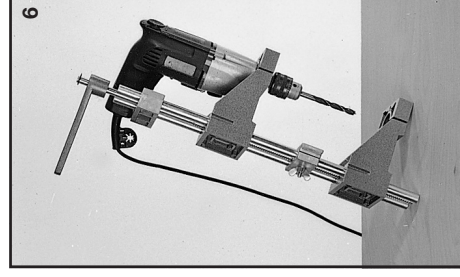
Arbeiten mit einem Motor, einer Bohrmaschine oder einer Oberfräse (evtl. Systembacke umdrehen).
